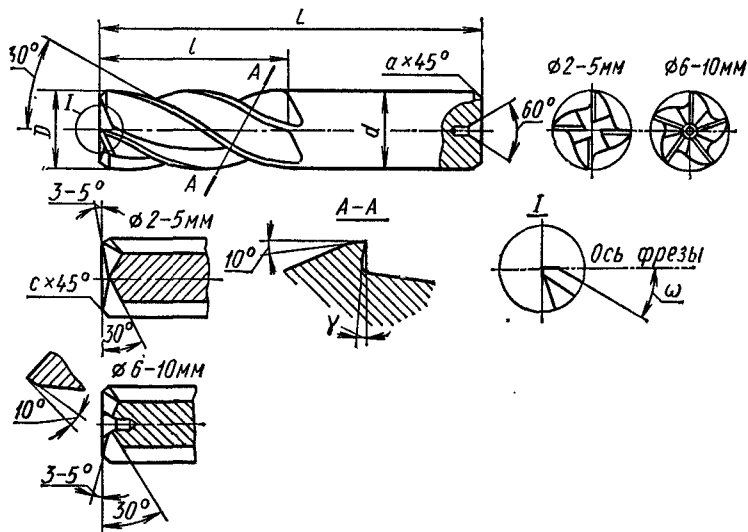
Цельнотвердосплавная концевая фреза с вышлифованными канавками
